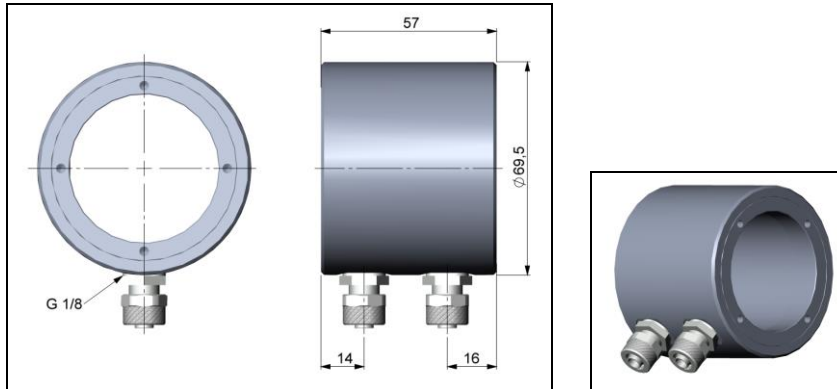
Wasserkühlgehäuse [Bestell-Nr.: ACCTLW] Schlauchanschluss: 6x8 mm Gewinde (Fitting): G 1/8 Zoll
